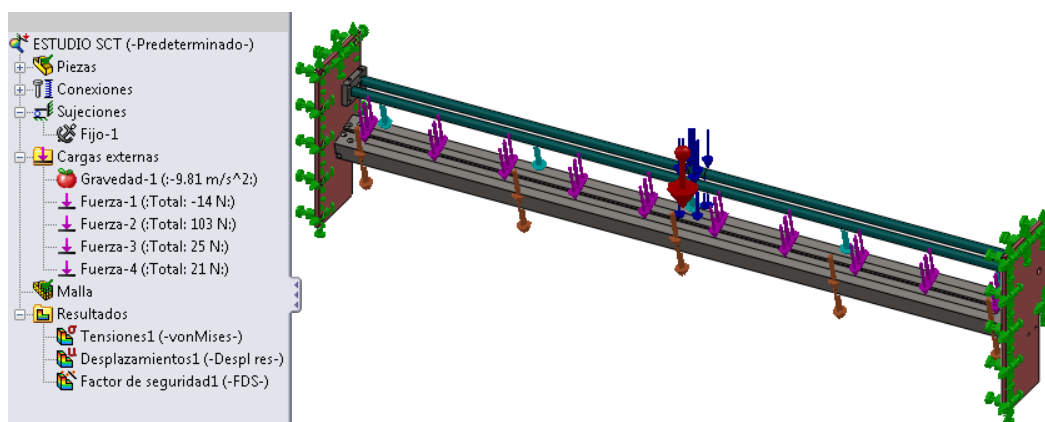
Cargas y restricciones - Sistema de corte transversal.
